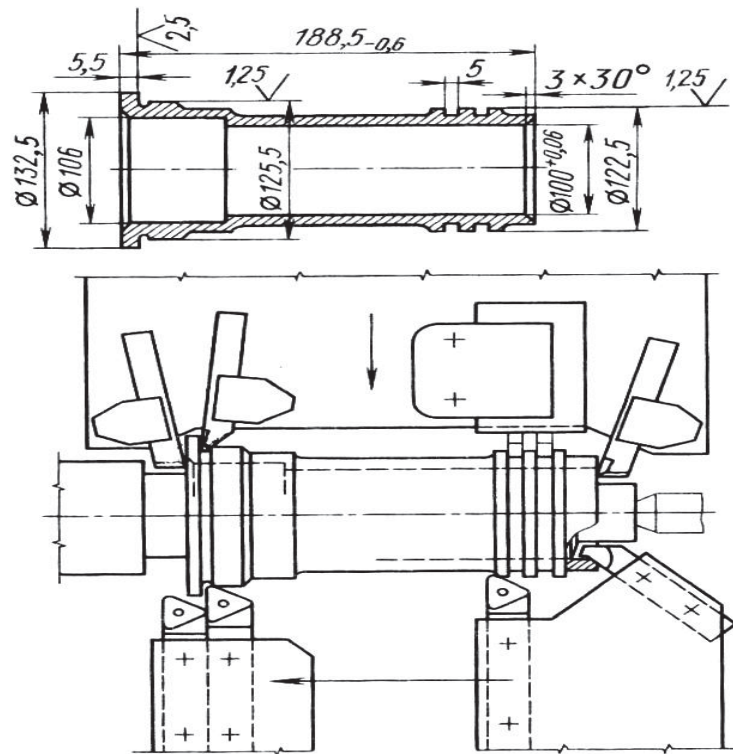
Наладка напівавтомата 1A730 для обробки гільзи циліндрів двигуна
